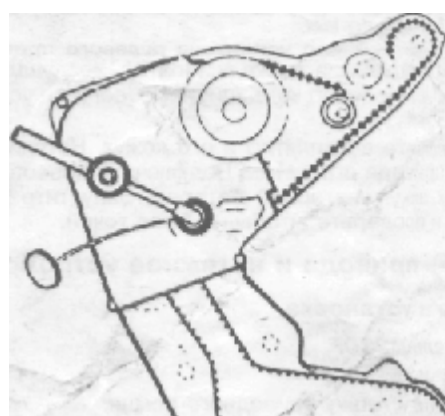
Регулировка натяжного устройства ремня привода — Двигатель В234F
